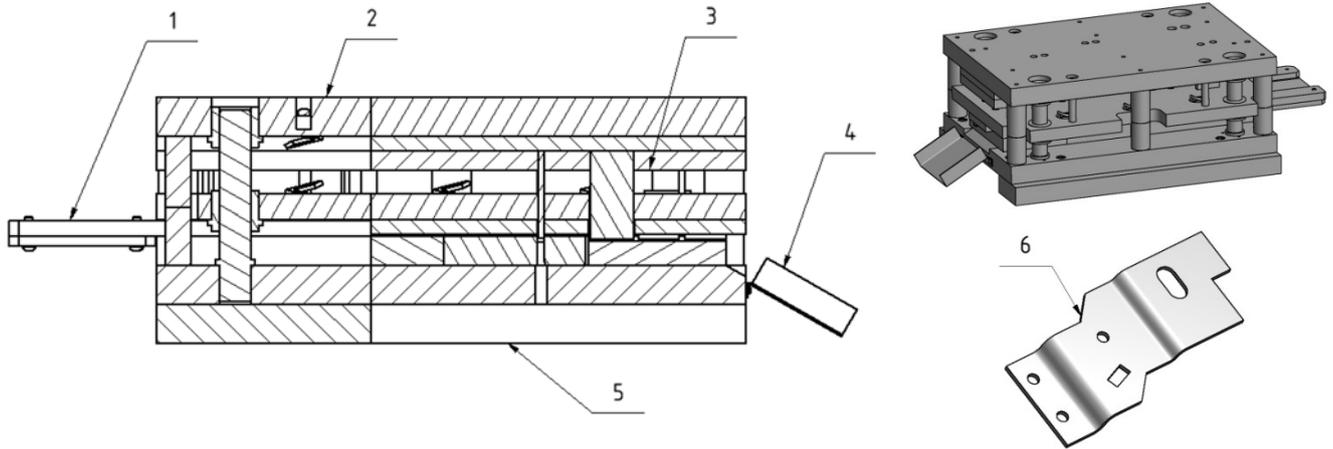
Lochwerkzeug mit Keilschieber für Deckel
